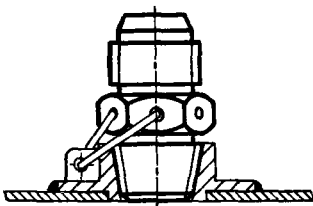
Стопорение вязкой штуцера с конической резьбой
